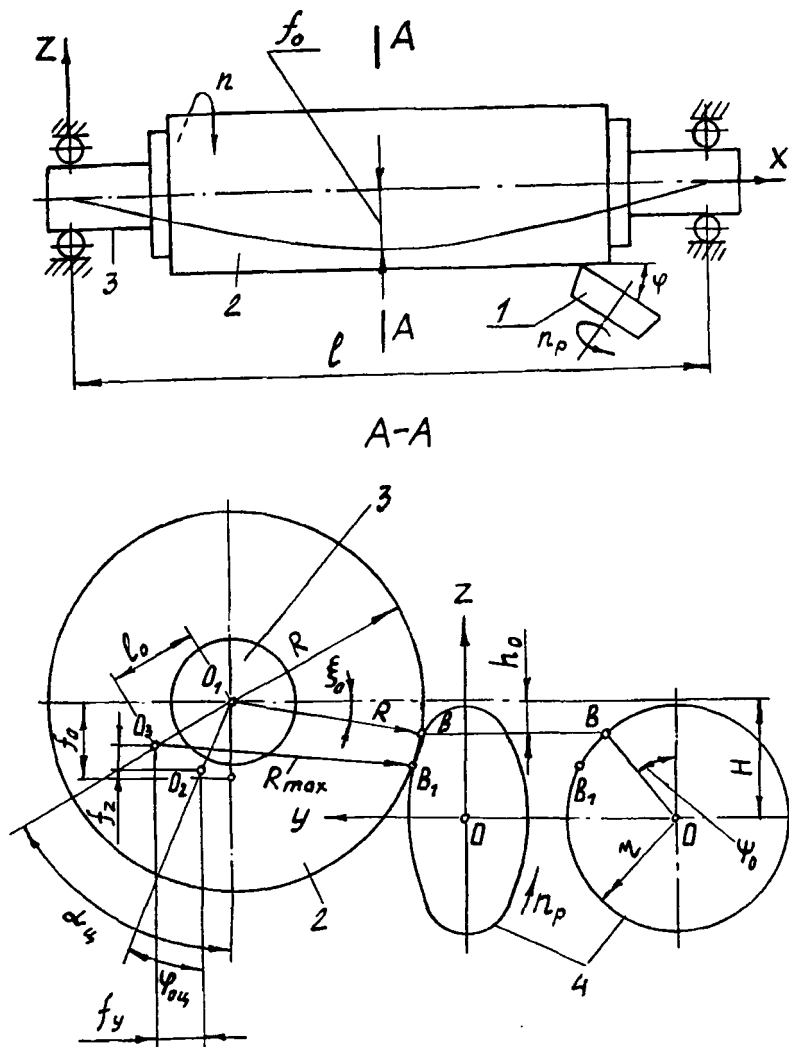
Расчетная схема к определению точности обработки каландрового вала (1 – резец; 2 – бумажный цилиндр; 3 – стальной вал; 4 – режущая кромка резца)
